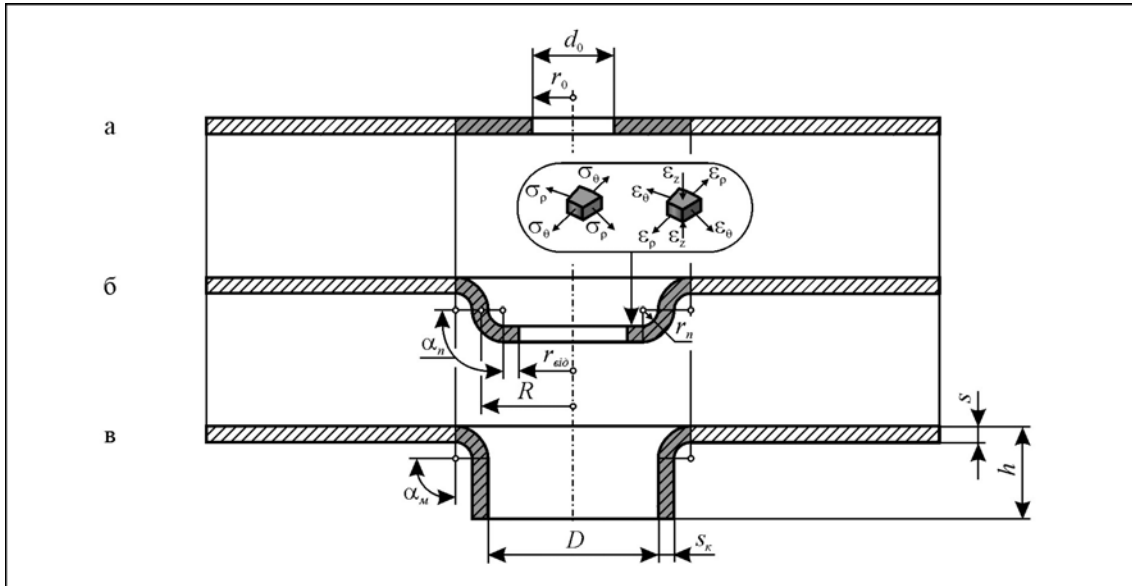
Морфологія зміни форми заготовки в процесі відбортування: а – вихідна заготовка; б – проміжна заготовка; в – заготовка після відбортування
